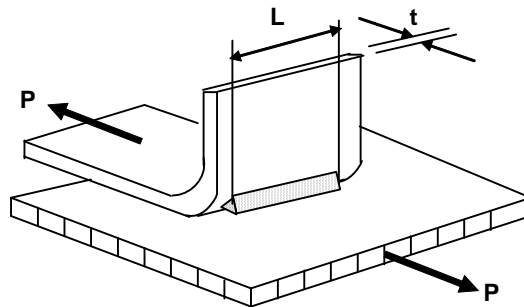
Soldadura a tope acampanada en bisel cargada transversalmente.
